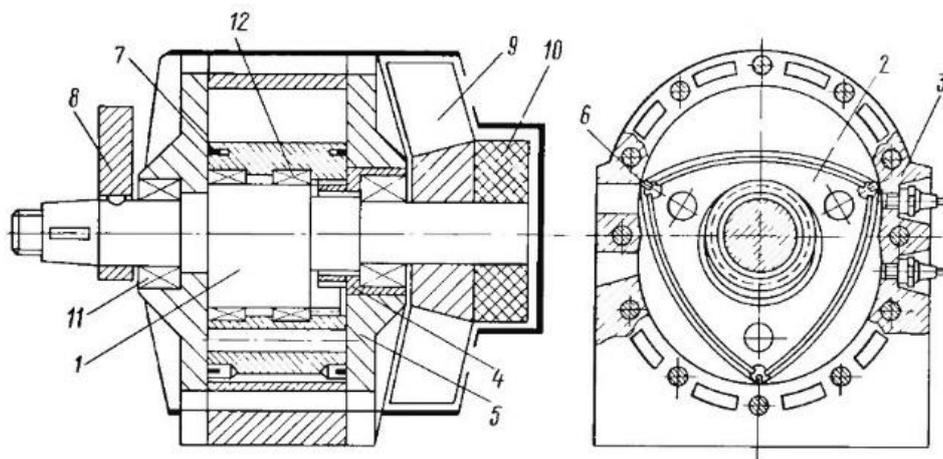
Схема конструкции роторного двигателя внутреннего сгорания.
